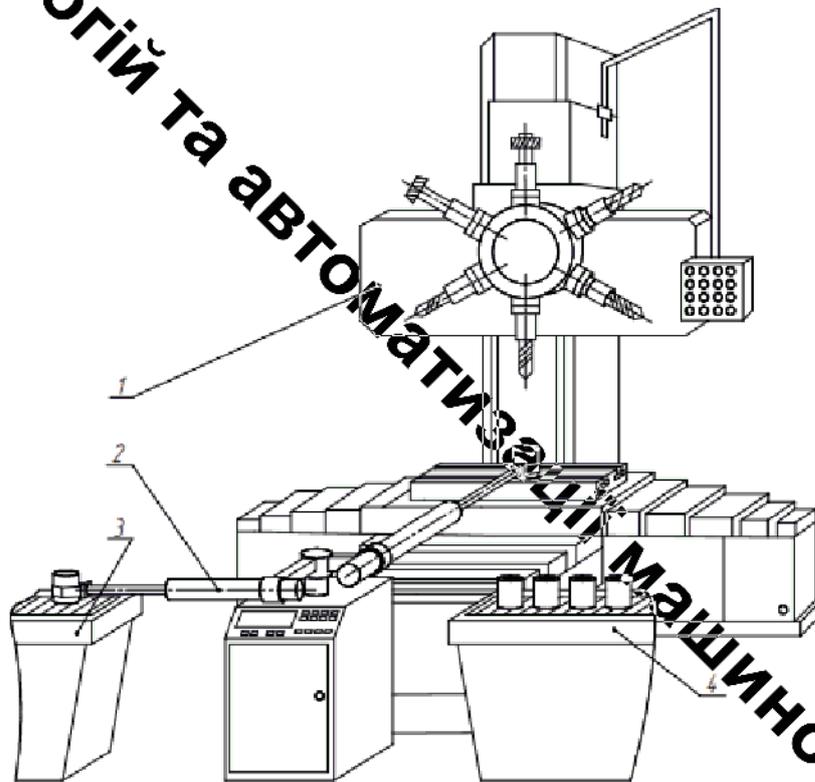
Автоматизоване робоче місце для свердлильно-фрезерної обробки
